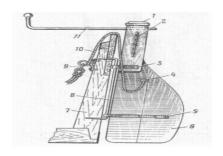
Рулевое устройство: 1 — головка руля; 2 — чека с цепочкой; 3, 5 — петли с оковками; 4 — отверстие для сорлиня; 6 — перо руля; 7 — ахтерштевень; 8 — стержень; 9 рым кормового фалиня; 10 — сорлинь; 11 —румпель
